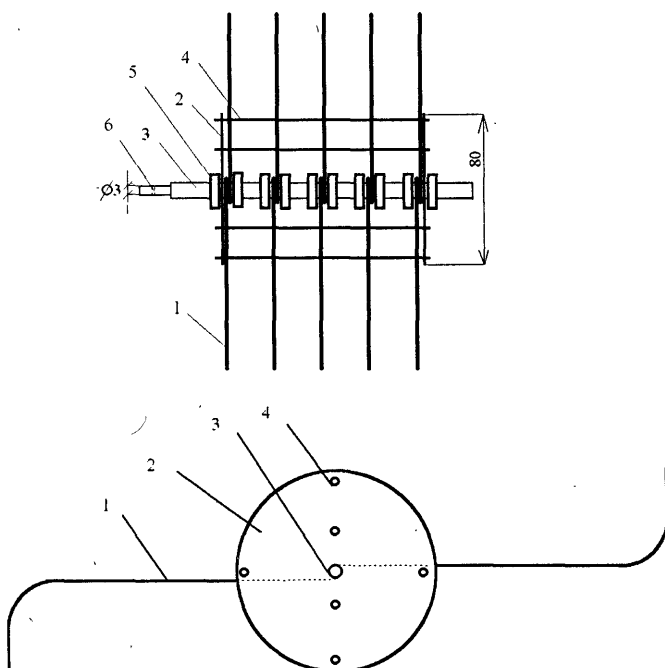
Барабан сброса и подъема груза: 1 — спица; 2 — щечки; 3 — вал; 4 — распорки; 5 — гайки; 6 — отверстие под шплинт
